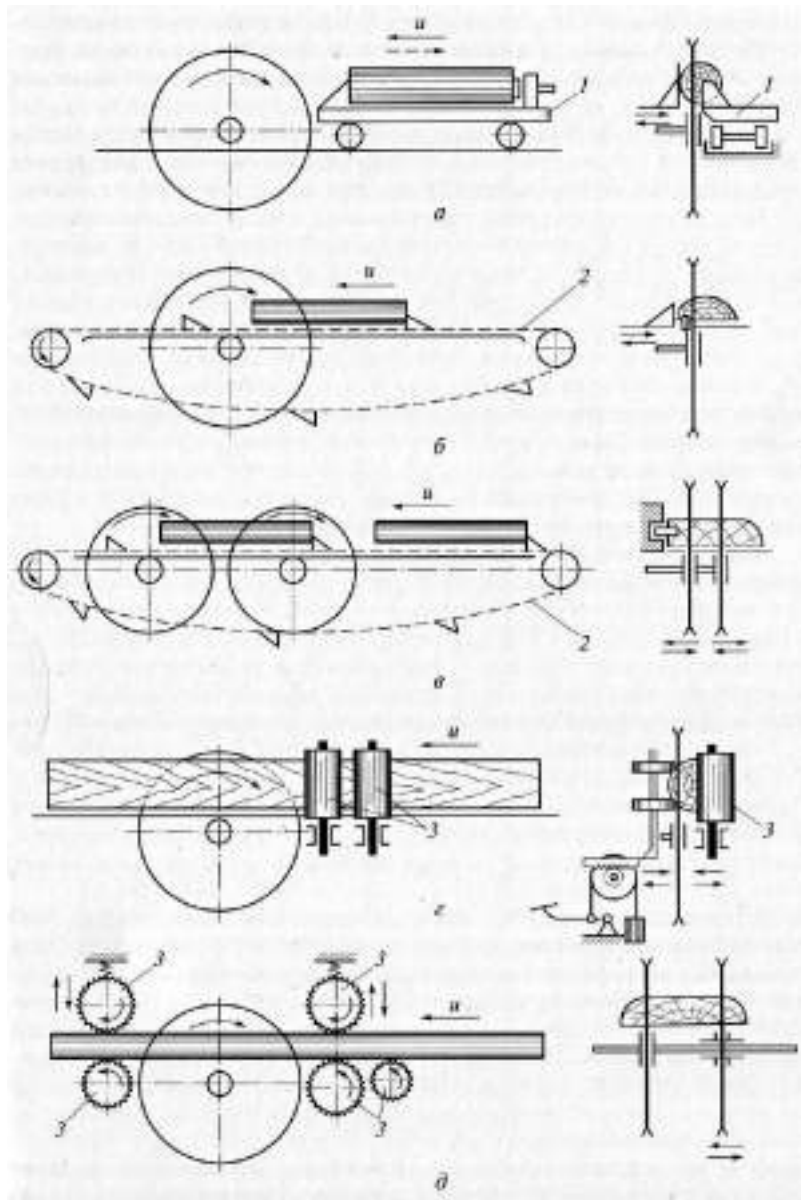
Схемы круглопильных станков для продольной распиловки:
